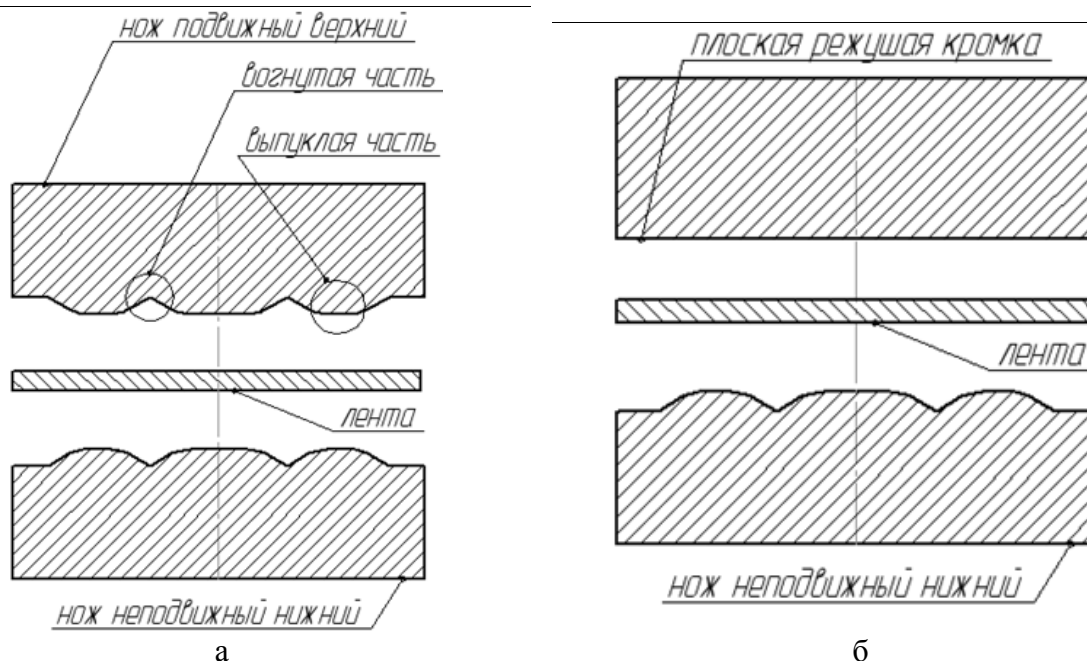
Конструктивное исполнение ножей для надреза сдвигом неспрофилированной движущейся ленты: а – с зеркально выполненными режущими кромками; б – плоскими режущими кромками
